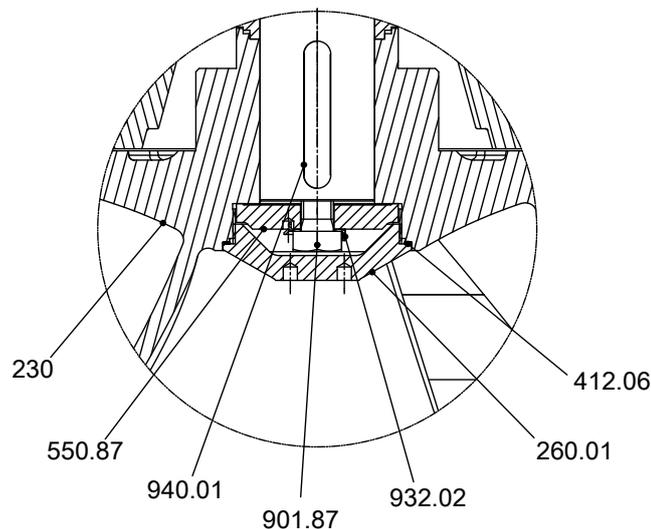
Laufradbefestigung, Baugrößen: 1000-420, 1000-500, 1200-630
